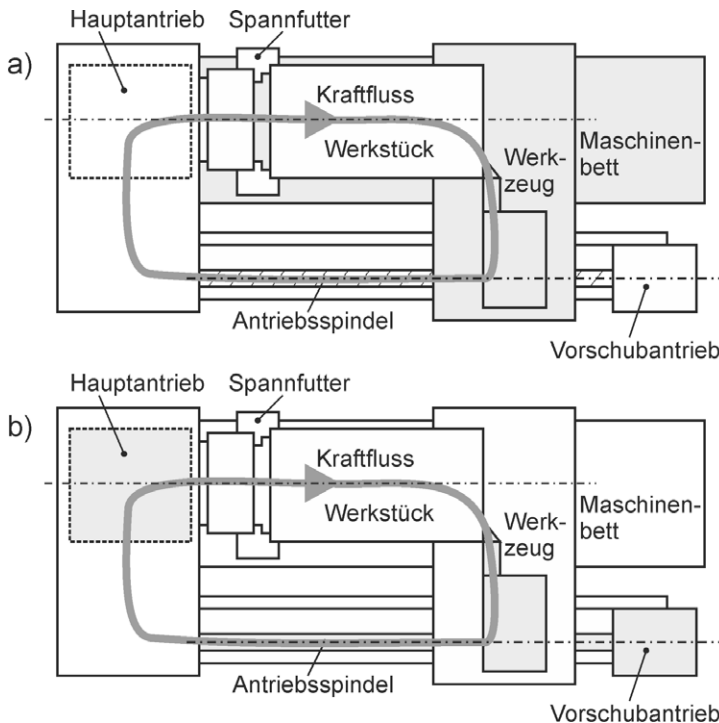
Schematische Draufsicht einer Drehmaschine mit Baugruppen im Kraftfluss a) grau unterlegt maschinenbauliche Maßnahmen b) grau unterlegt elektrotechnische Maßnahmen
